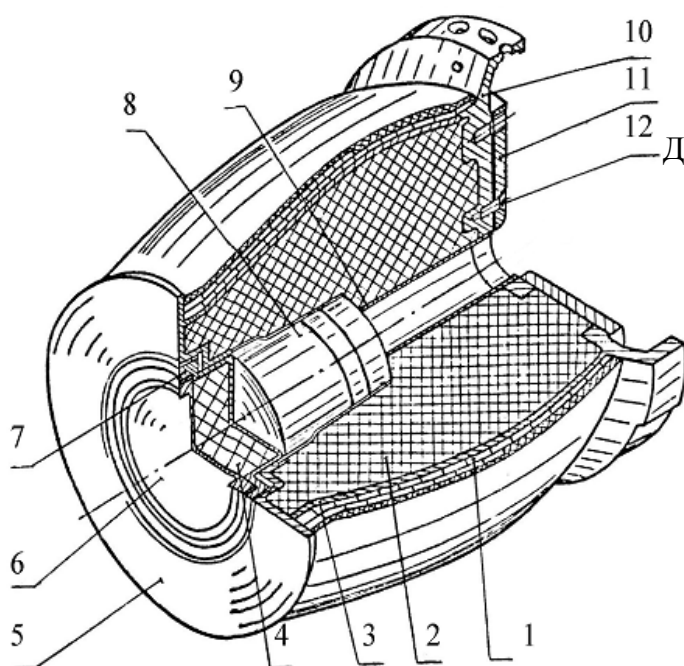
Боевая часть: 1 – поражающие элементы; 2 – заряд ВВ; 3, 9 – оболочка; 4 – шашка; 5, 10 – фланец; 6, 11 – крышка; 7 – гайка; 8 – ПИМ; 12 – винт
